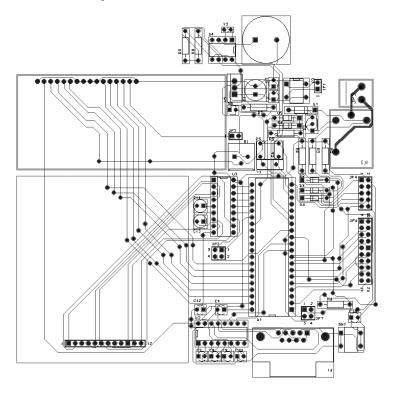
Diseño en Orcad Layout de la segunda tarjeta.
